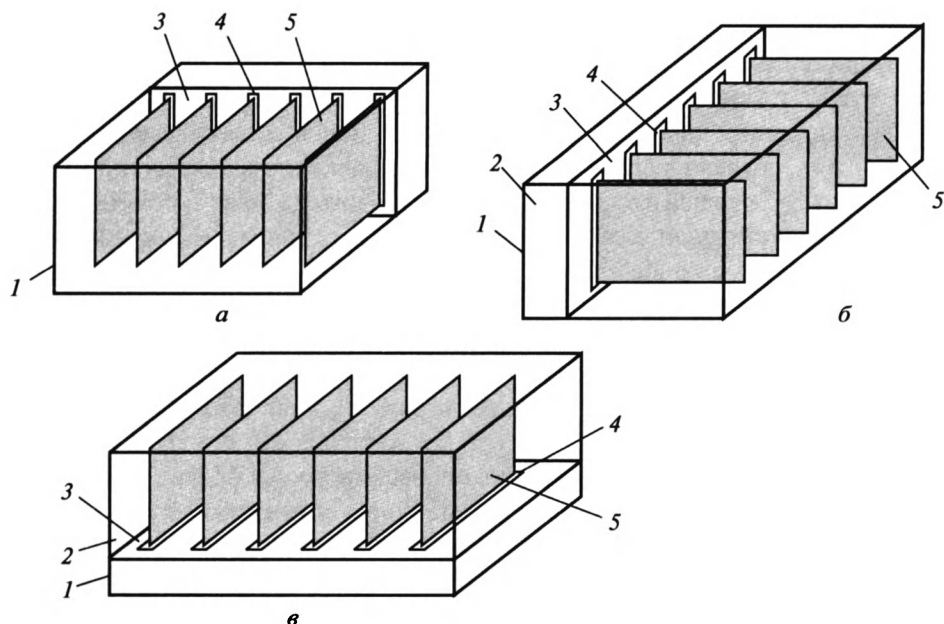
Вертикальное поперечное (а), вертикальное продольное (б), горизонтальное (в) расположение монтажной панели блоков стеллажной конструкции:
